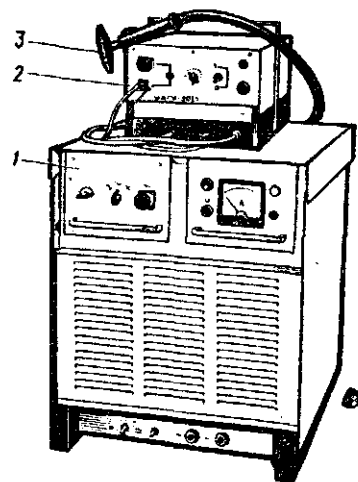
Универсальная установка УДГУ-301 для ручной аргонно-дуговой сварки алюминиевых сплавов:
